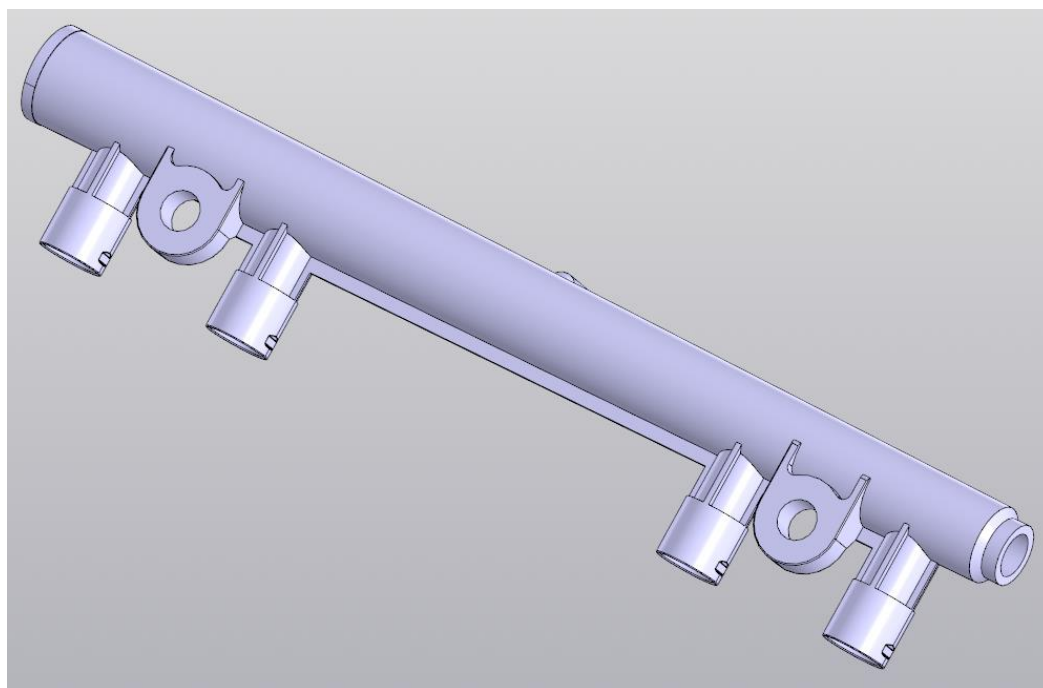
3D модель корпуса топливной рампы (вид сзади)
